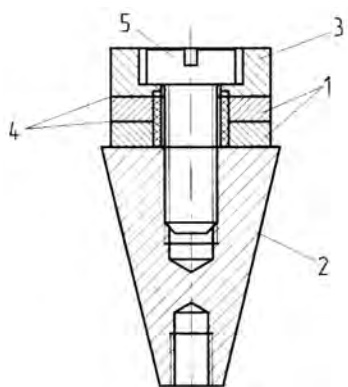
Конструктивное исполнение полуволнового пьезокерамического преобразователя продольных колебаний: 1 – пьезокерамические пластины; 2 – излучающая накладка; 3 – отражающая накладка; 4 – контактная пластина; 5 – стягивающий центральный болт
